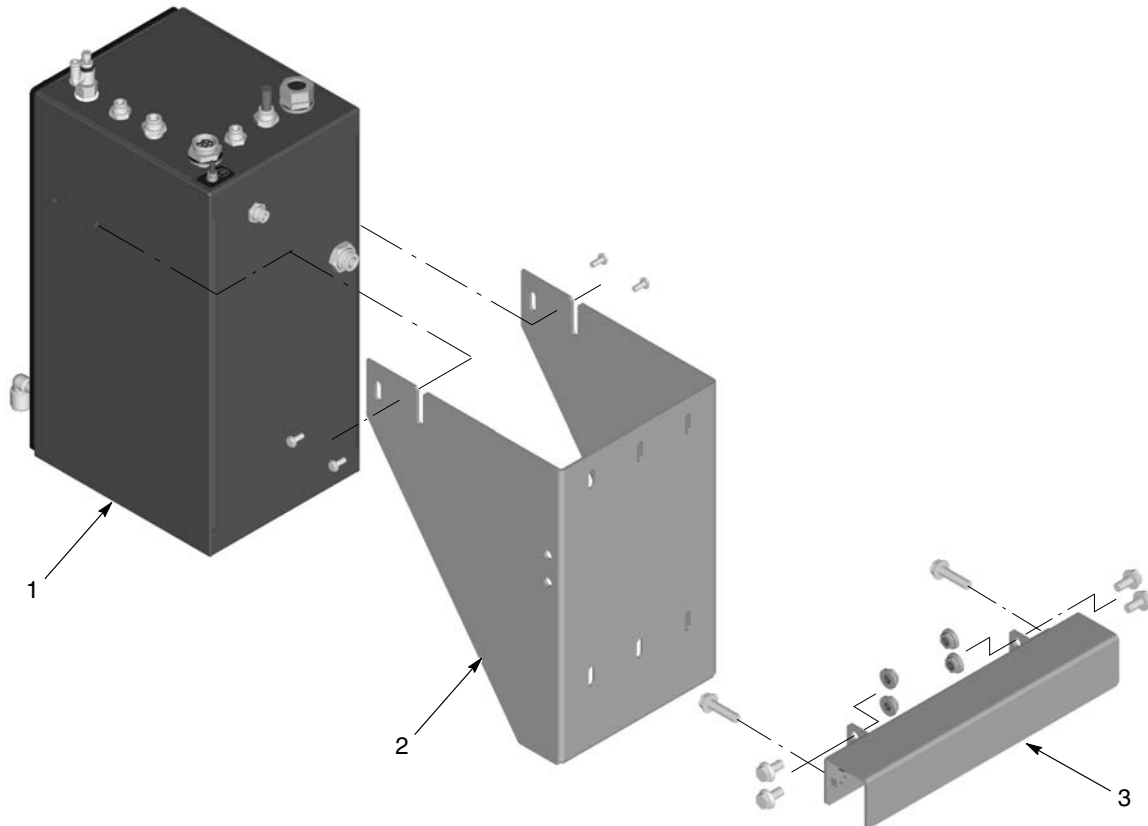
Halterungen für Wandmontage des Pumpensteuergerätes
